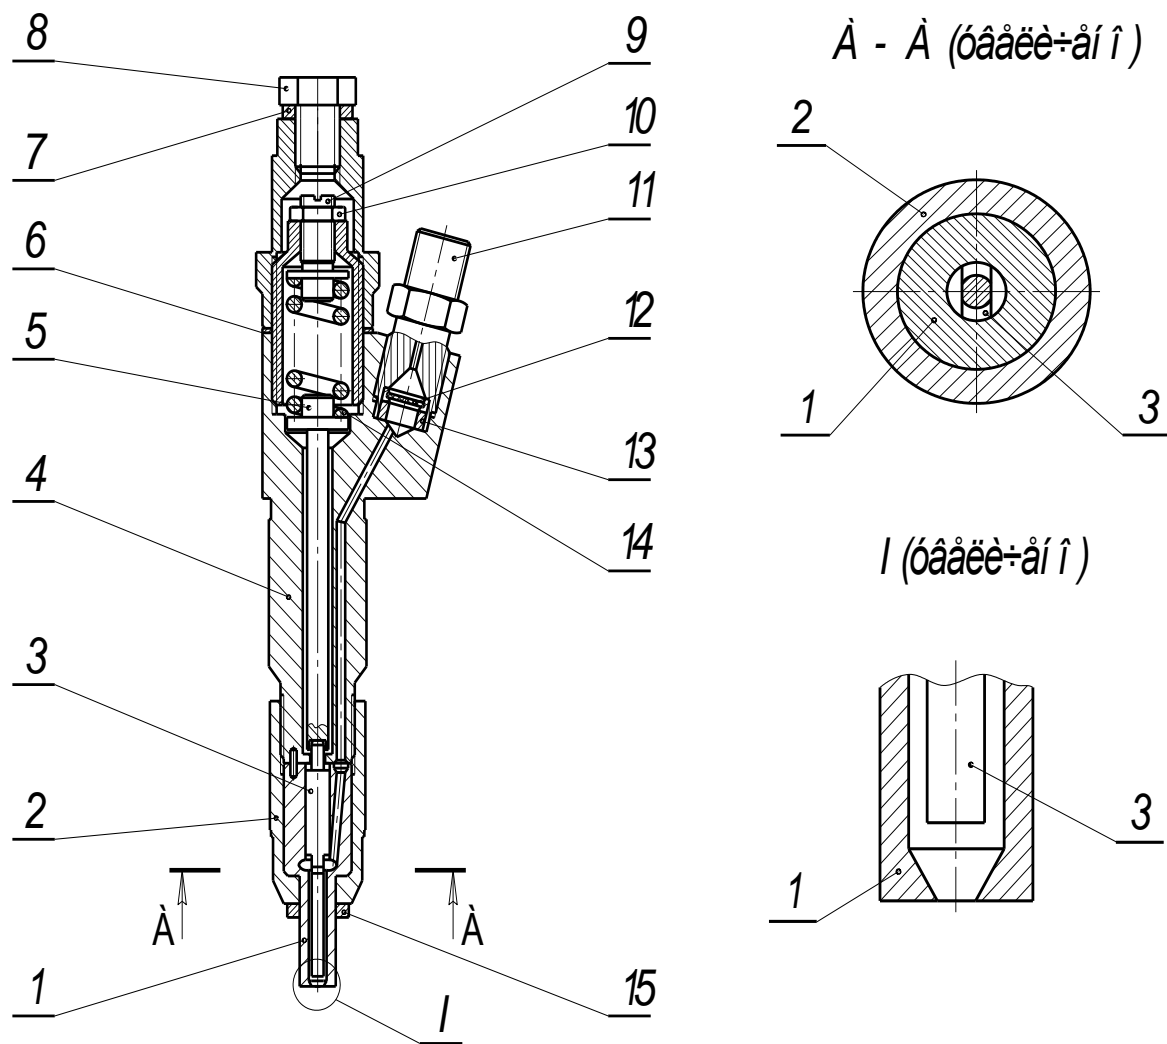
Фальшь-форсунка «с иглой распылителя» двигателя Д-240:
